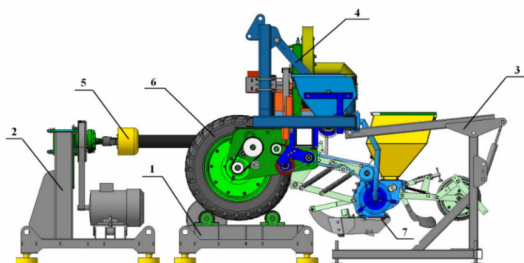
Схема установки сеялки точного высева на стенд:
